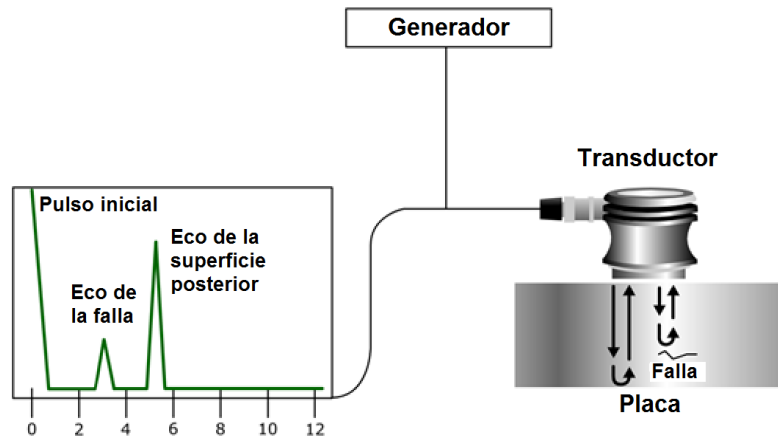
Componentes del equipo de ultrasonido [4].
